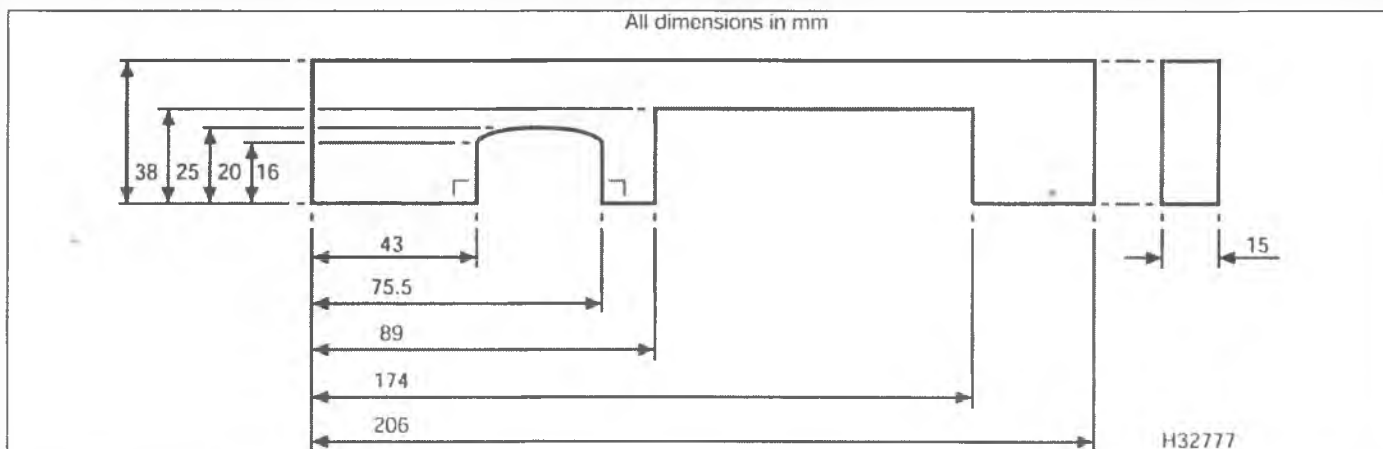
,а. Размеры инструмента для выверки положения распределительного вала (все размеры в миллиметрах)
